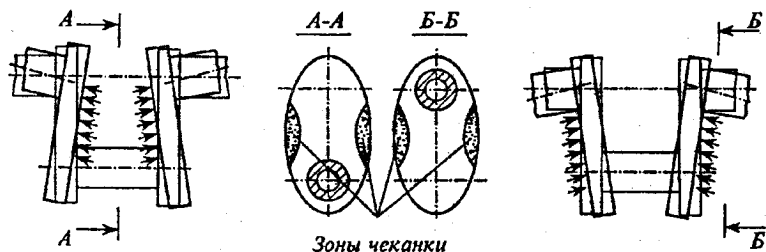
Правка коленчатого вала наклепом (чеканкой)
